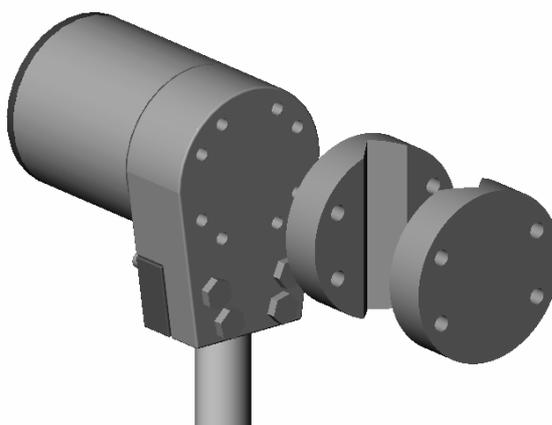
Démontez les cales de serrage de la barre de montage pour une installation sur le malaxeur
